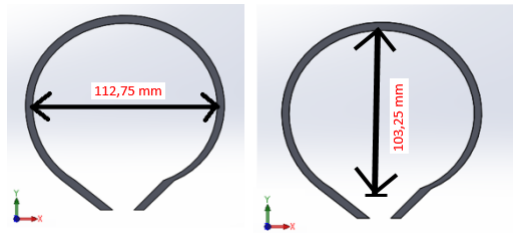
Ferramenta Cotada. (SolidWorks)
